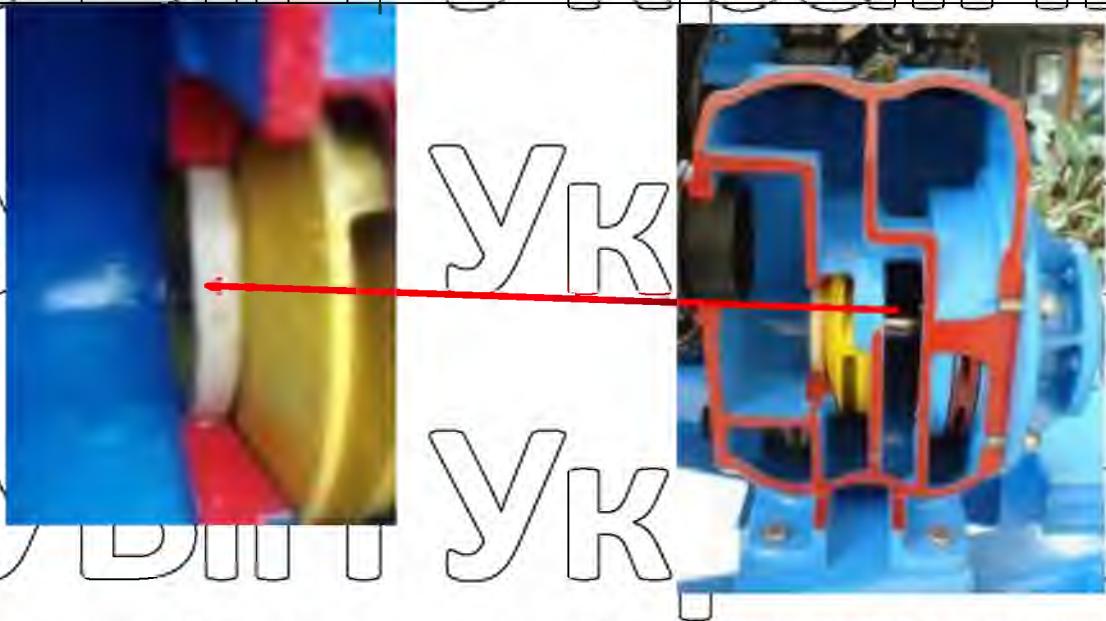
додаткова опора вала насоса OMEGA підшипник ковзання
